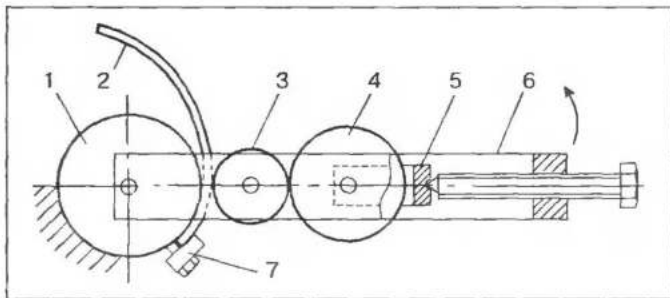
Схема работы простого приспособления для гибки вкладышей:
